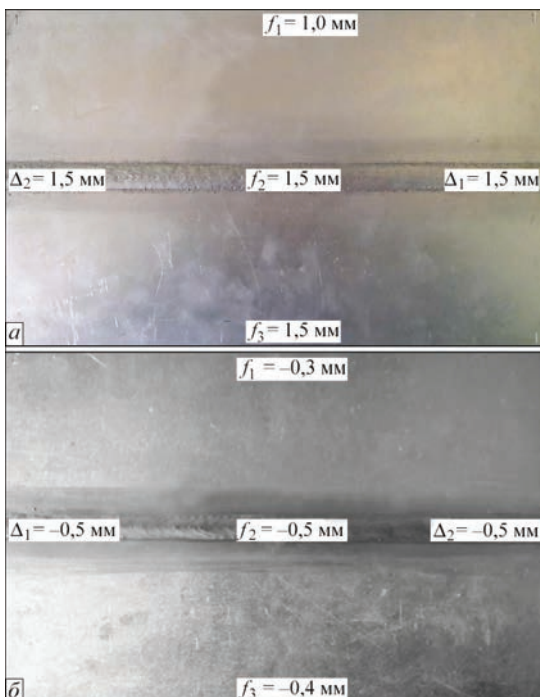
Внешний вид лицевой поверхности и геометрические характеристики сварных соединений пластин из сплава 1561, выполненных дуговой (а) и гибридной плазменно-дуговой сваркой (б)
